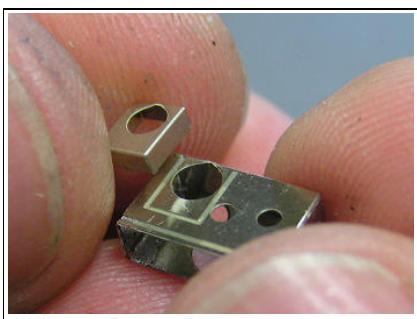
Der gebogene Motorhalter soll genau in die geätzten Nuten des Getriebe- kastens passen. > Test
